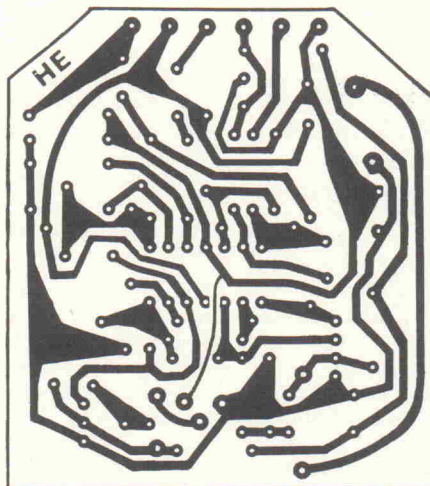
Das Platinen-Layout für den Gitarren-Phaser.
